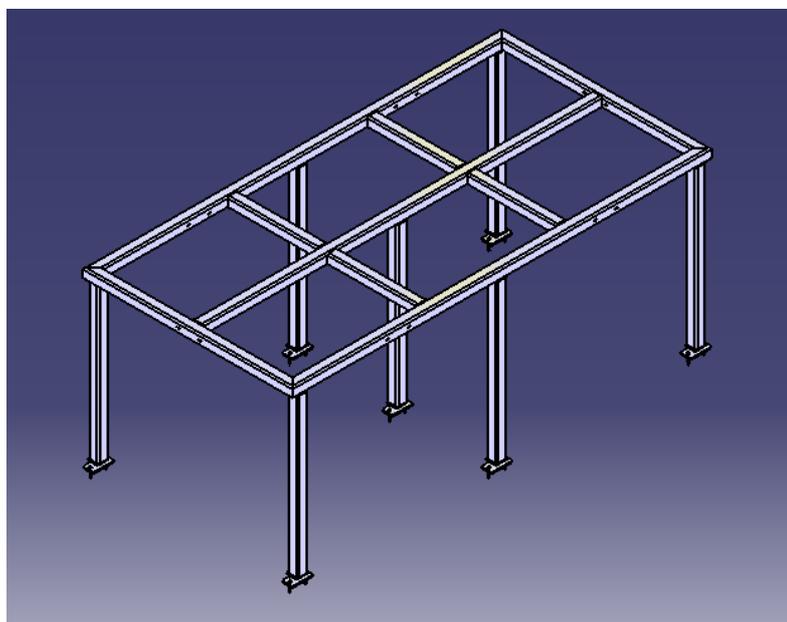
Estructura del módulo 11111.03.000 soldada
